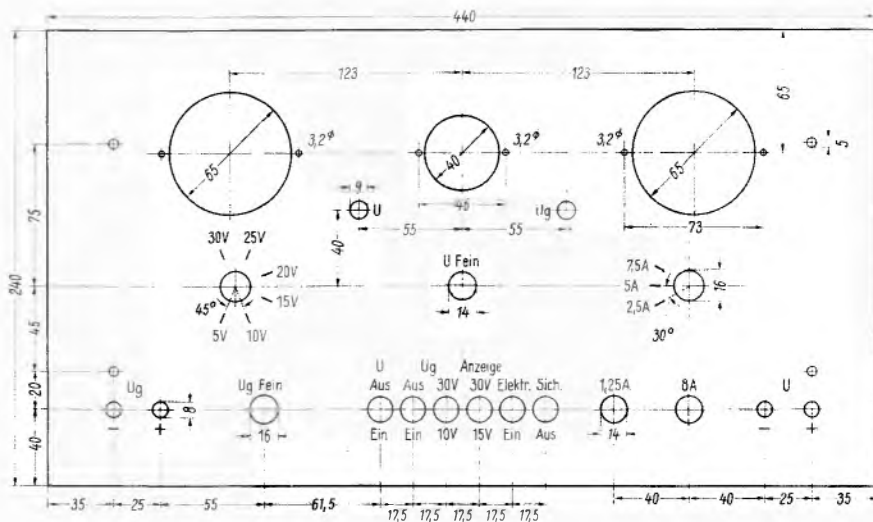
Abmessungen und Bohrungen der zweiten Frontplatte
